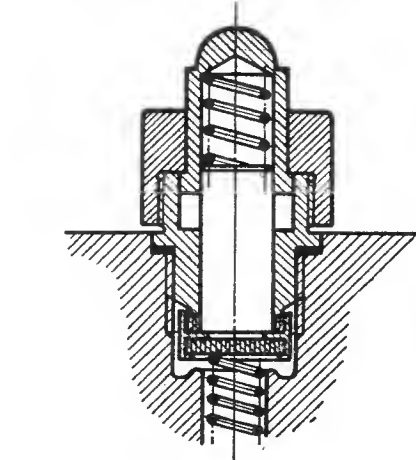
Nockenventil für Direktdruck mit Druckausgleich
